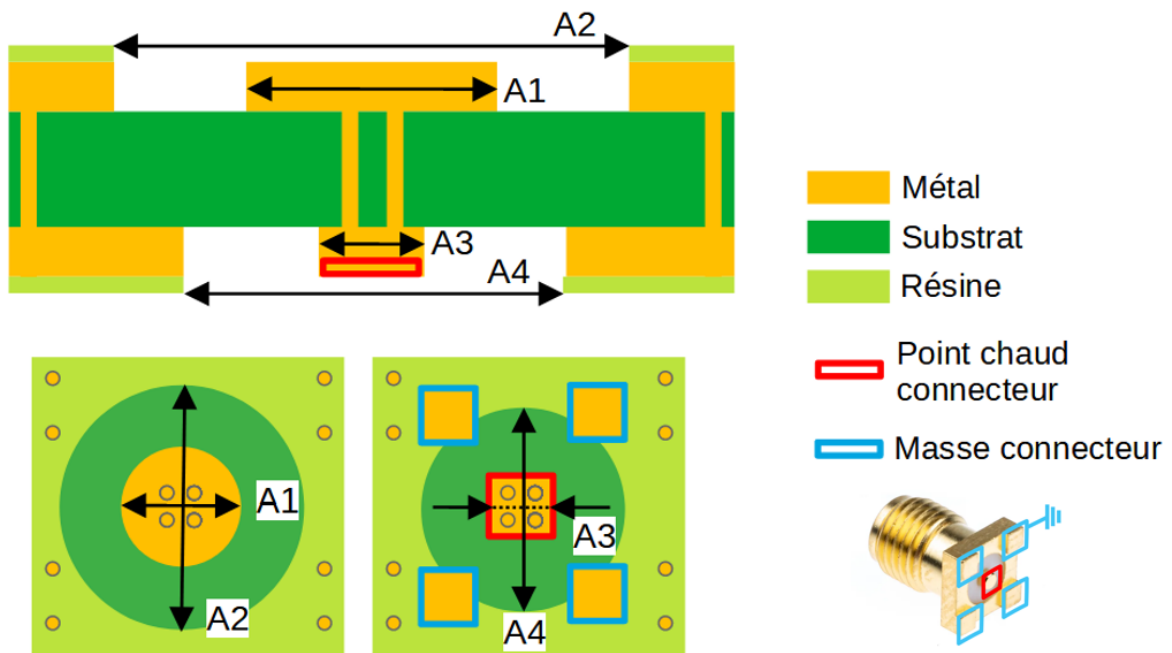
Schémas techniques d'un applicateur RF dit « simple » et ses dimensions: en haut, vue en coupe ; en bas à gauche, vue de dessus ; en bas à droite, vue de dessous
